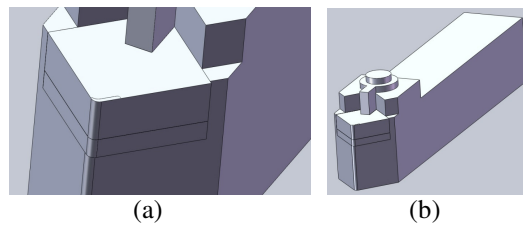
Conjunto ferramenta de corte, calço e suporte: (a) Detalhe da ferramenta de corte e sua interface de contato (b) Vista geral do conjunto.
